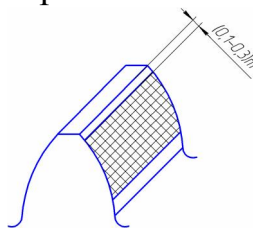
Форма и расположение пятна контакта зубьев цилиндрических зубчатых колес (m -модуль)
